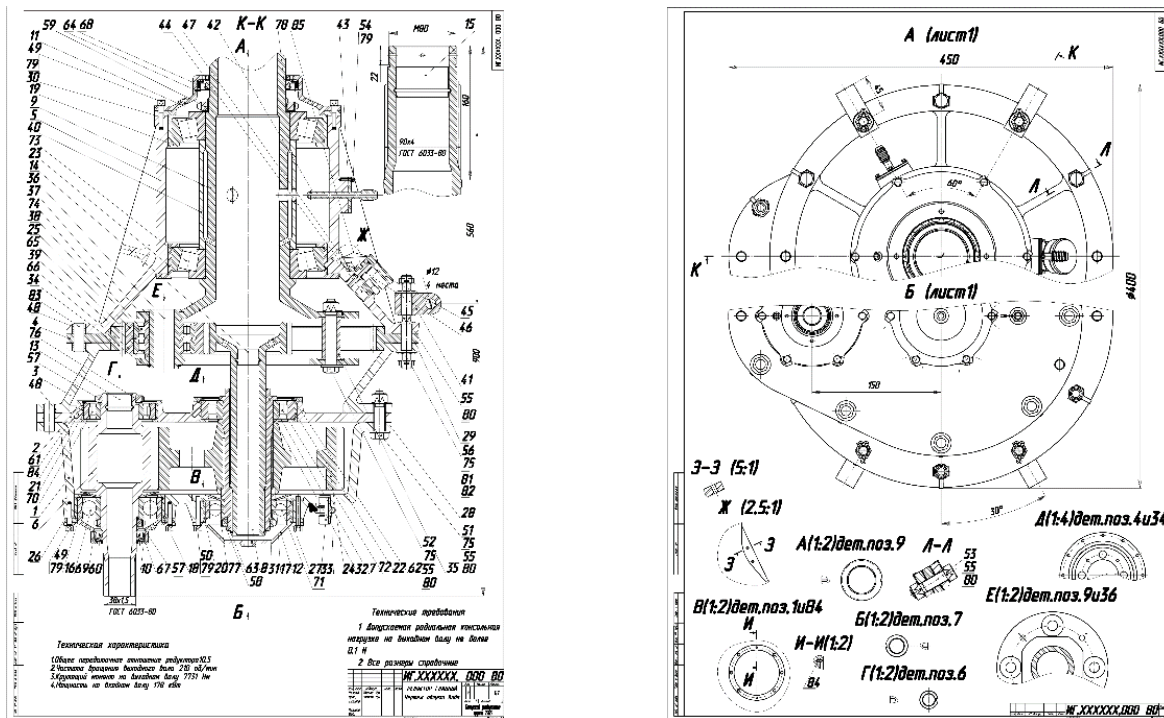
Чертёж общего вида редуктора (фрагмент)
